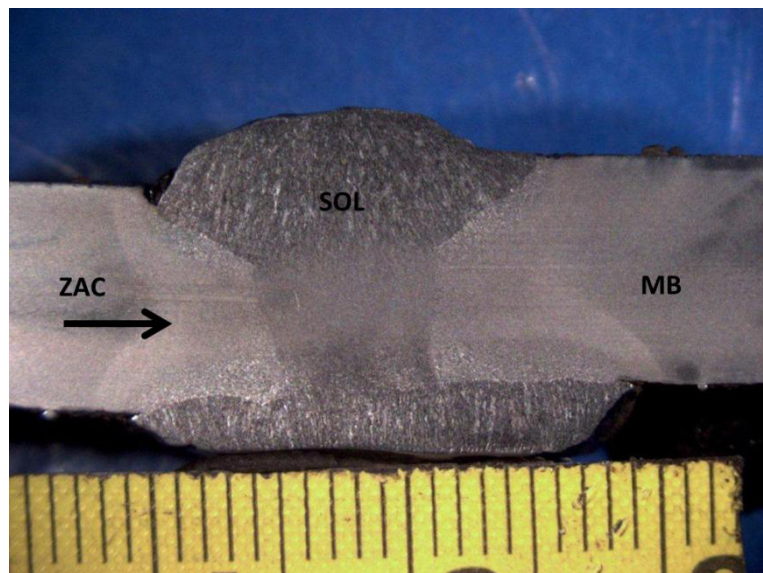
Macroataque de la soldadura del proceso SMAW.
